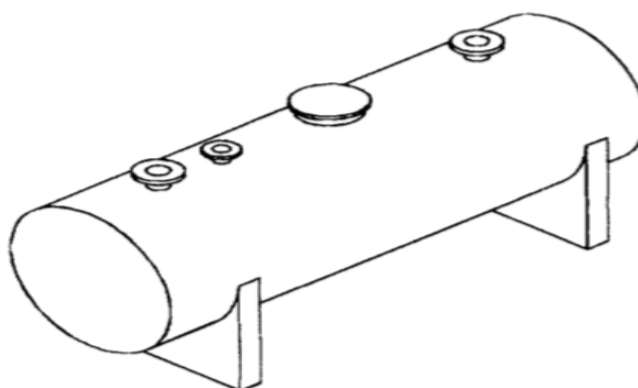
Tanque Horizontal-Tank and Vessel Handbook- Process Fabricators Inc.
